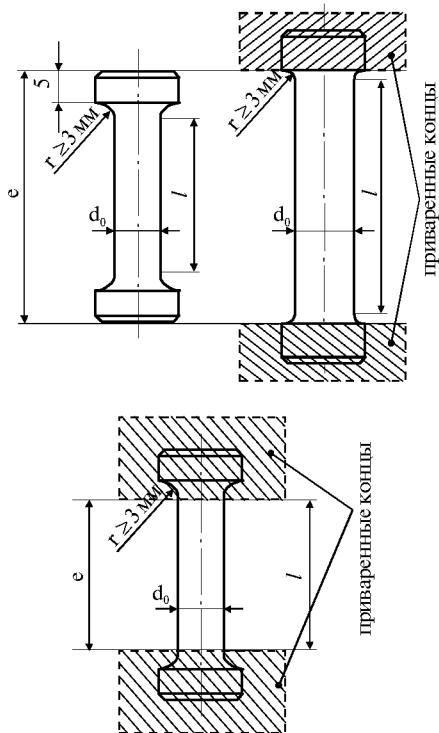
Варианты вырезки образцов для испытания на растяжение из листового проката по стандарту ISO 7778-1983 (E)
